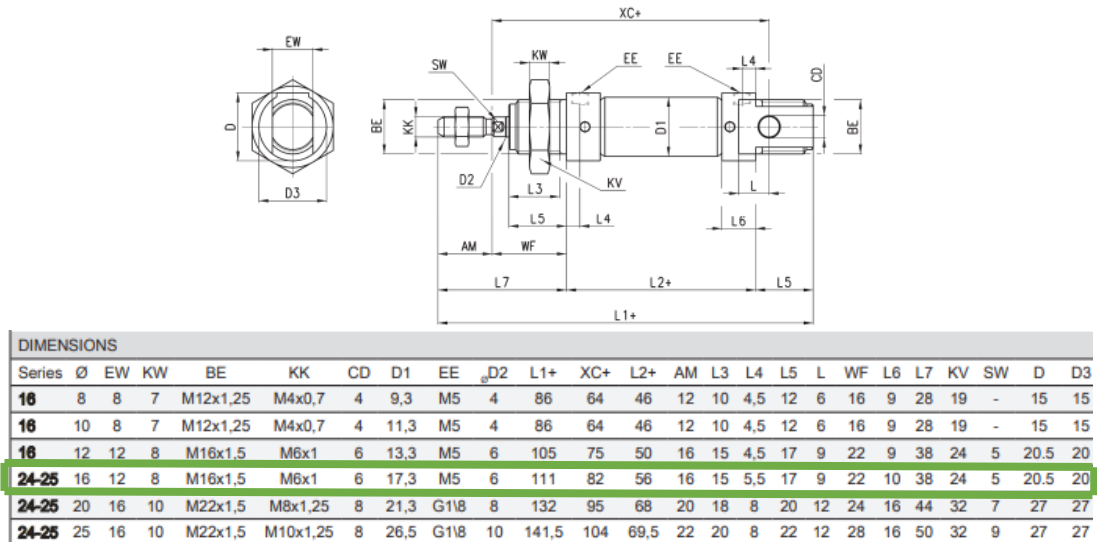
Dimensiones utilizadas para la selección del minicilindro neumático. [18]
